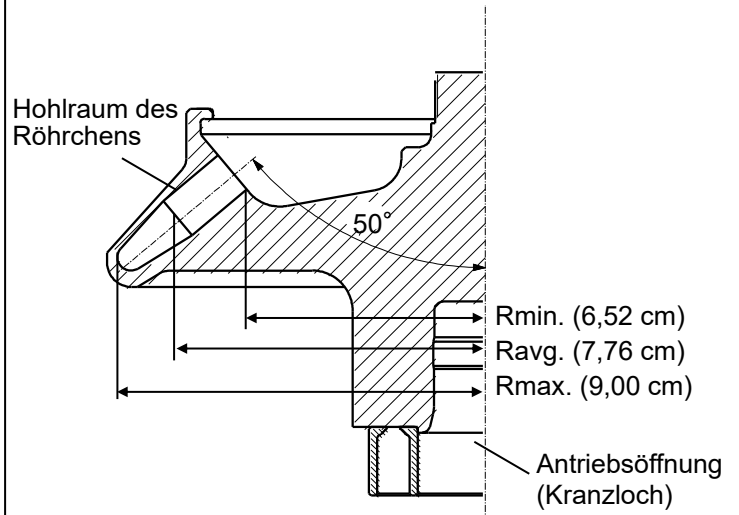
Querschnittsansicht des P50A3 Rotors
